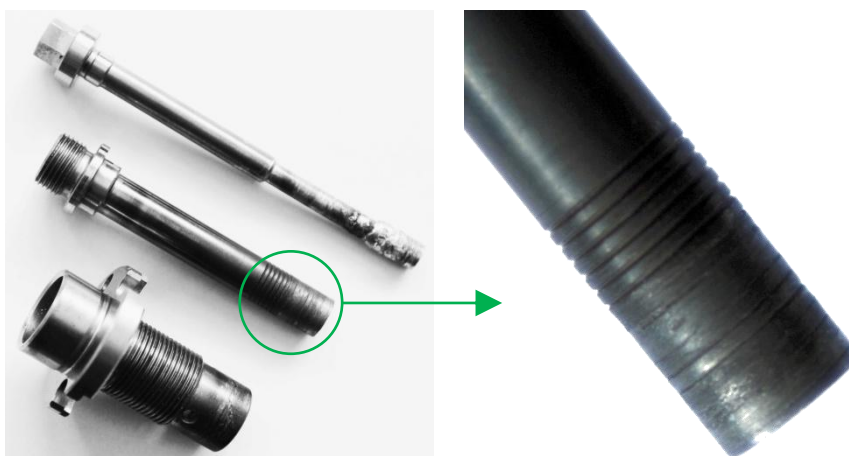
Ferramenta após o processo de soldagem com destaque para o desgaste da camisa.
